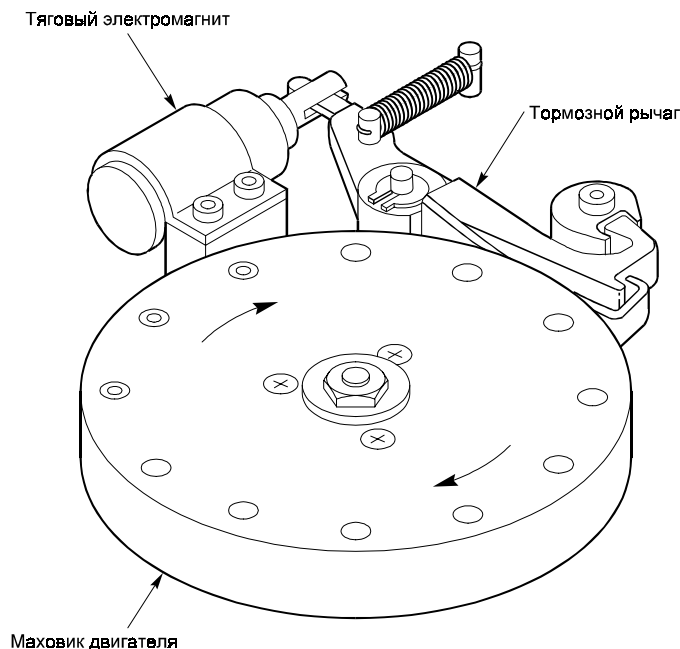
Электромагнитный тормоз шпиндельного двигателя
